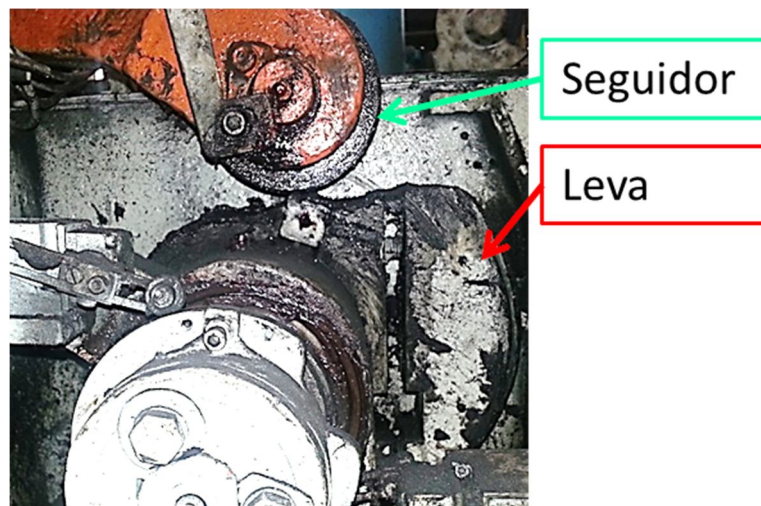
Sistema leva-seguidor soldador Swift-Ohio 91AA.
